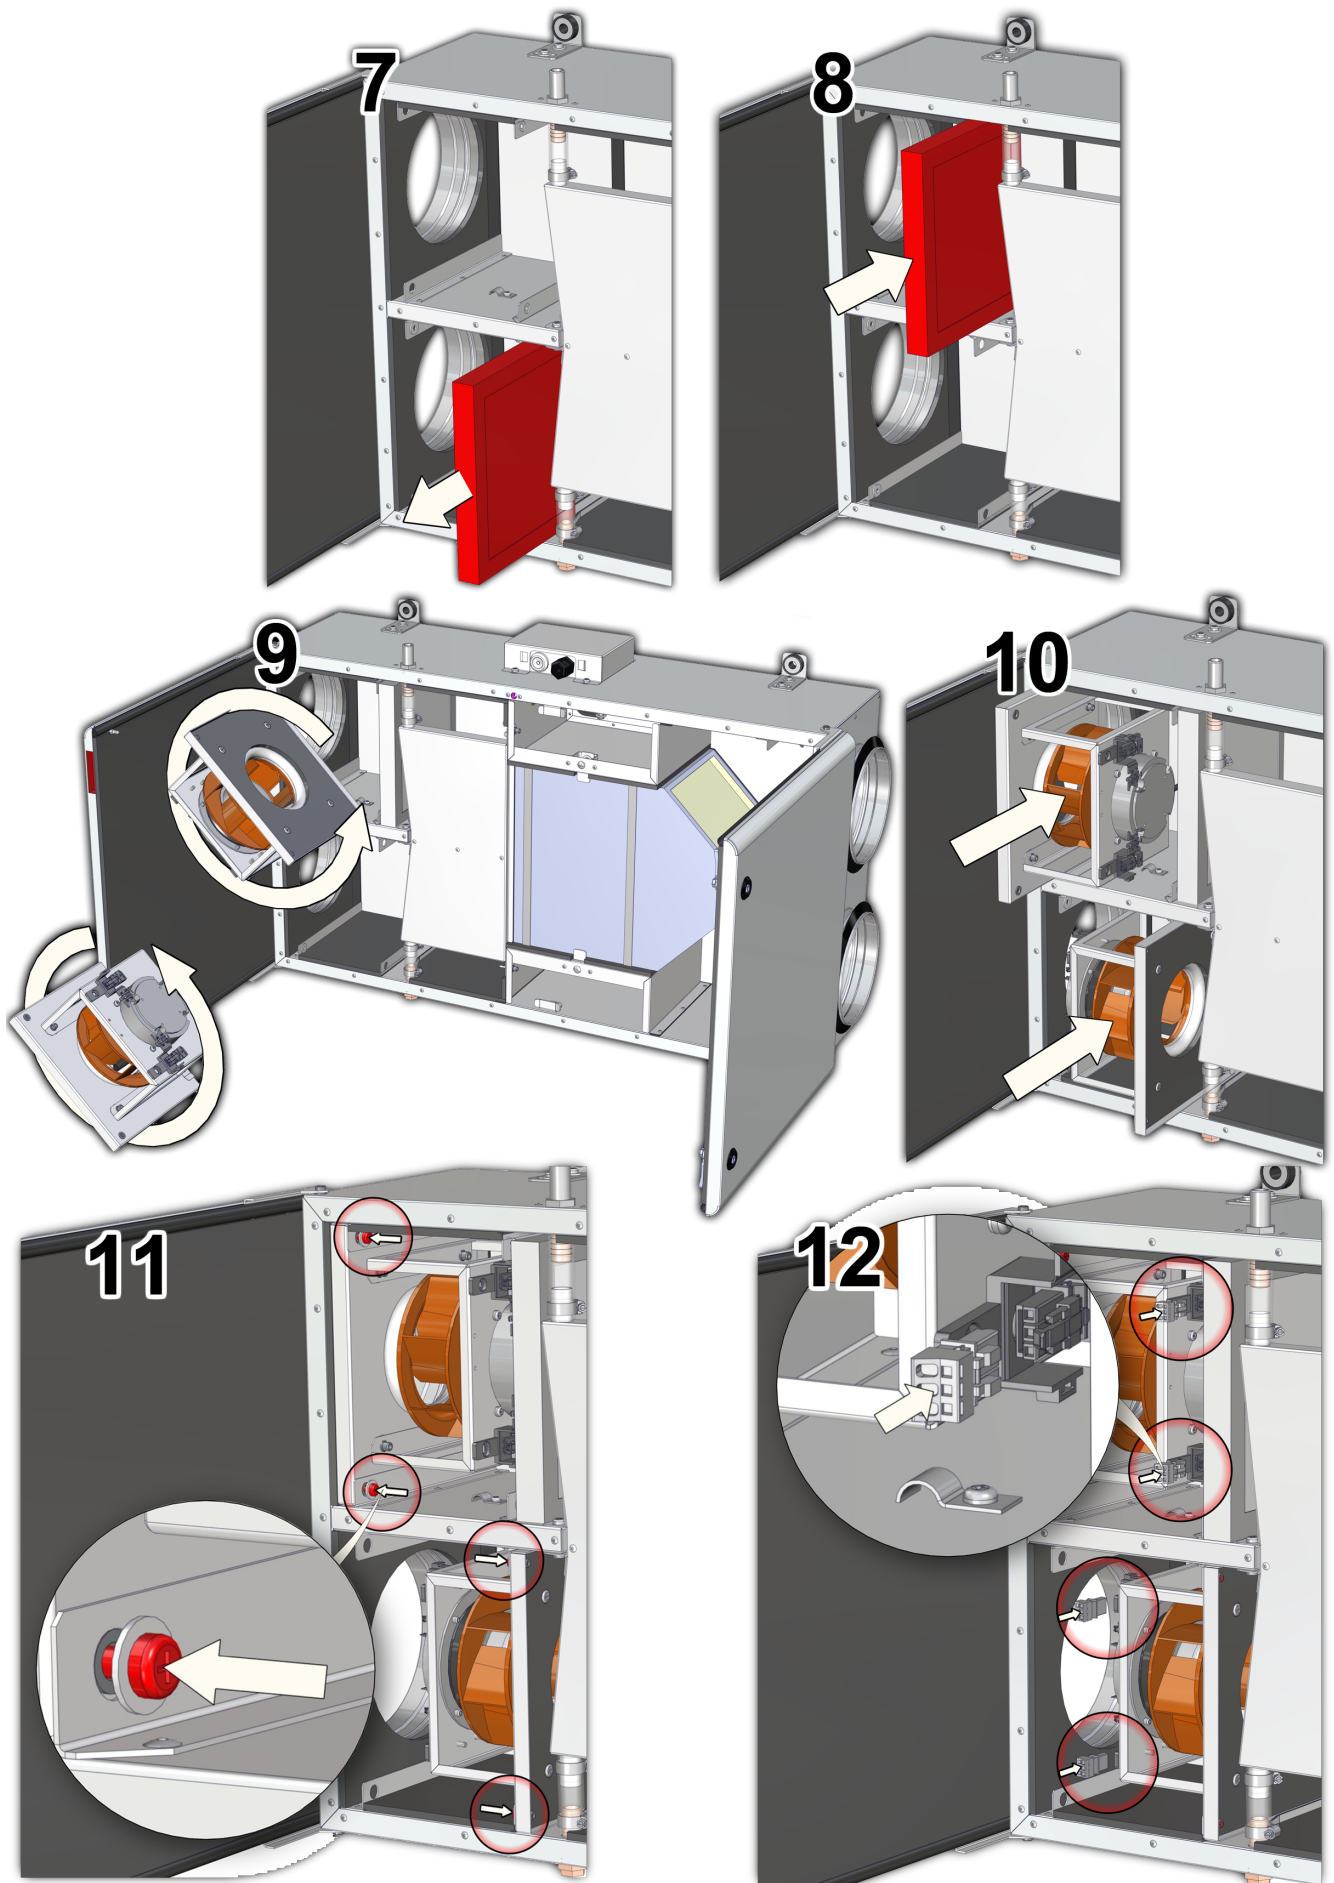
und 8: Ausziehbarer Filter (F7) der Zuluft (FRESH) wird ausgezogen und in den gewünschten Platz laut einem Schema eingesteckt. (Beim Einstecken des Filters auf die Richtung des Luftflusses, die auf dem Filter mit einem Pfeil gekennzeichnet ist, passen, die Richtung des Luftflusses im Aggregat ist im Flussschema gezeigt.)
